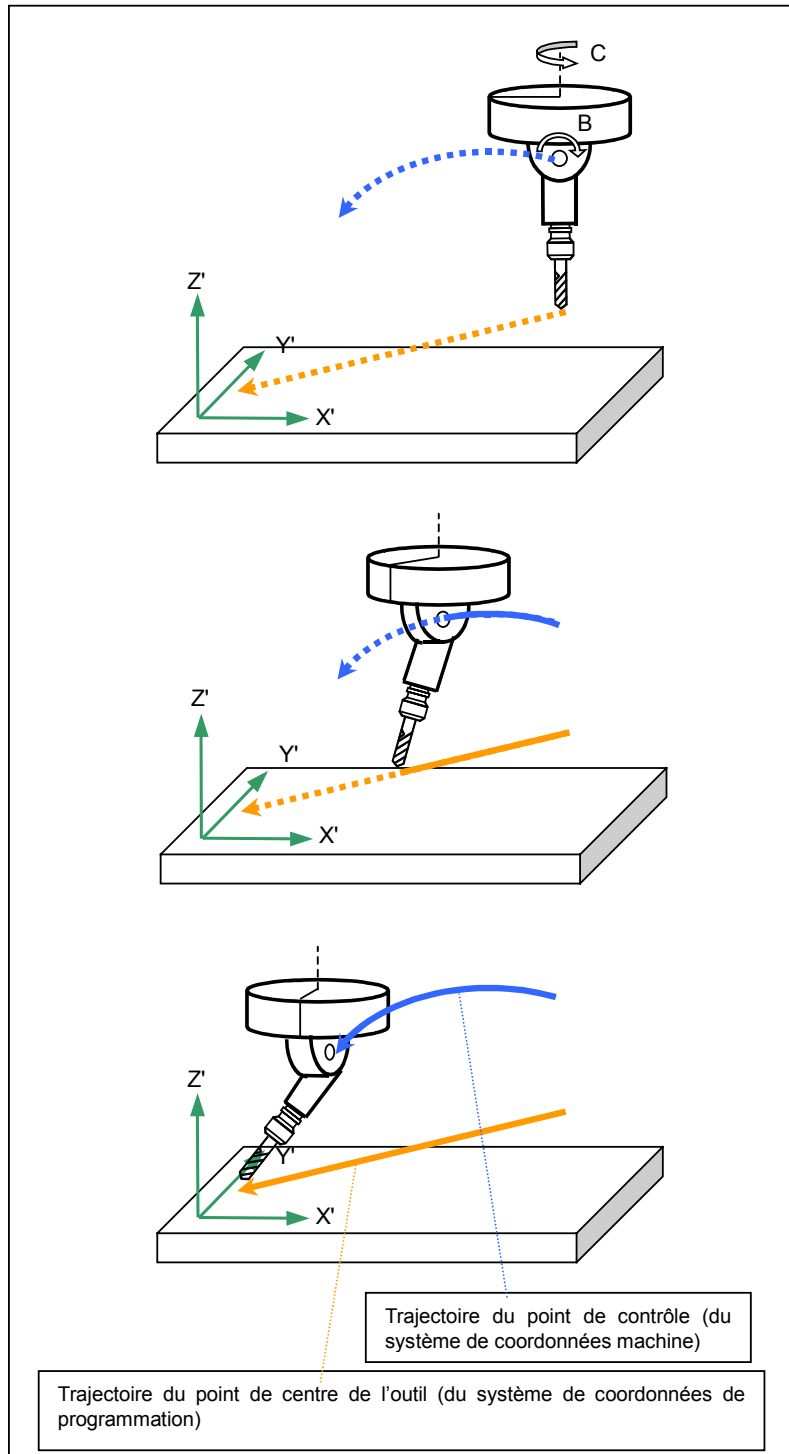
(j) Exemple pour une machine à outil rotatif
